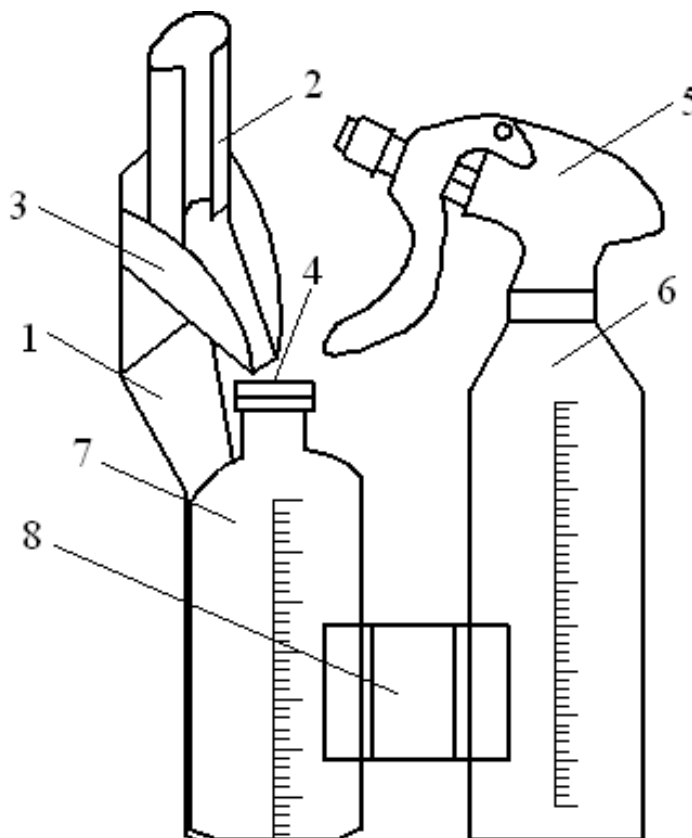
Конструктивна схема пристрою для визначення якості підготовки вимені корів до доїння
